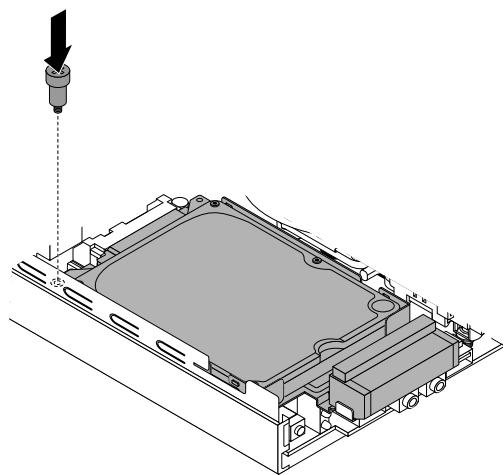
Instalación del tornillo del soporte de la unidad de almacenamiento
